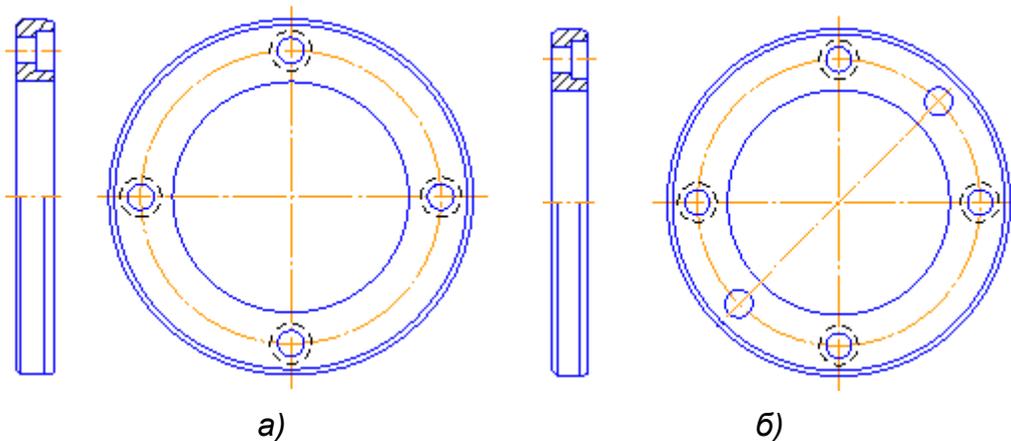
Конструкция фланца: а) — с посадкой; б) — без посадки.
